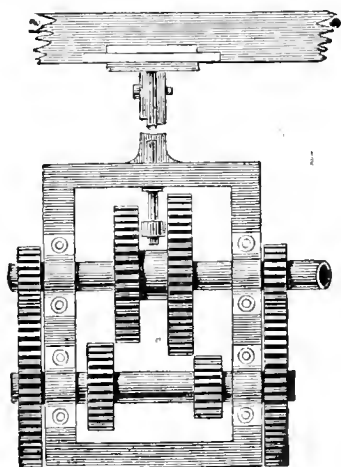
Engrenage mettant en mouvement les bras de la faneuse de MM. Ransomes, Sims et Head.
